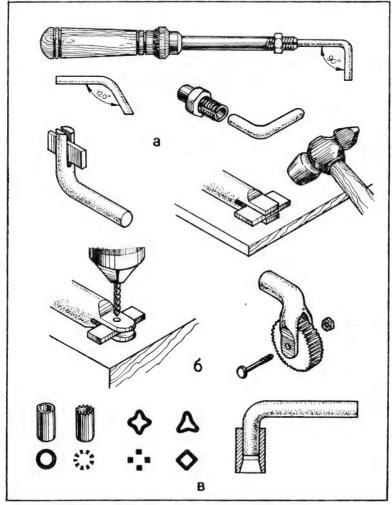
Изготовление приспособлений для пиротипии: а — устройство штемпеля со съемным наконечником; 6 — последовательность изготовления накатки; в — различные виды штемпелей
